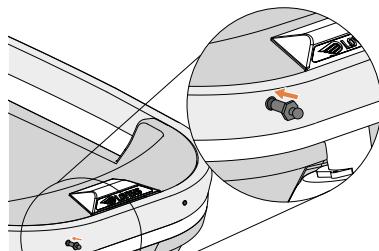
Befestigen des Bolzens mit Druckanschluss.
